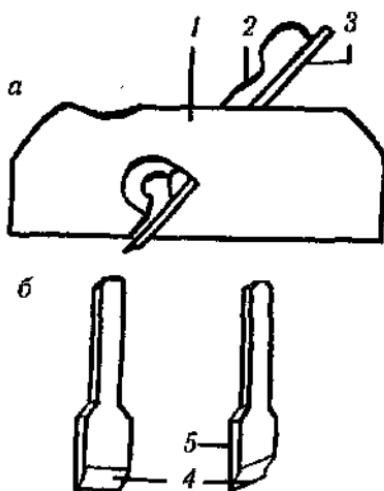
Зензубель: а — внешний вид; б — ножи с прямым и косым лезвием; 1 — колодка; 2 — клин; 3 — нож; 4 — фаски; 5 — боковая режущая кромка.
